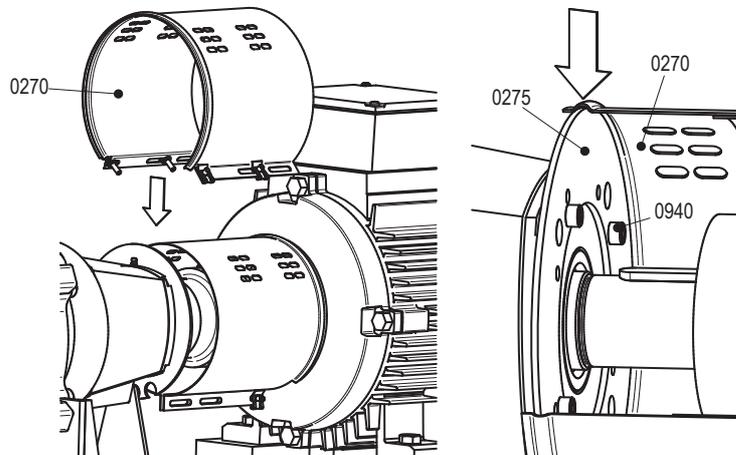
Montieren des Mantels auf der Pumpenseite.
